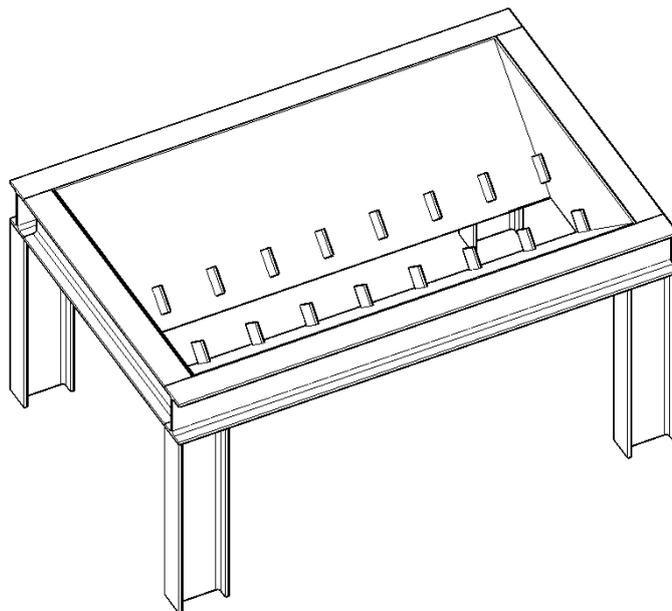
Tolva de llegada de los pistones. Fuente: elaboración propia.
